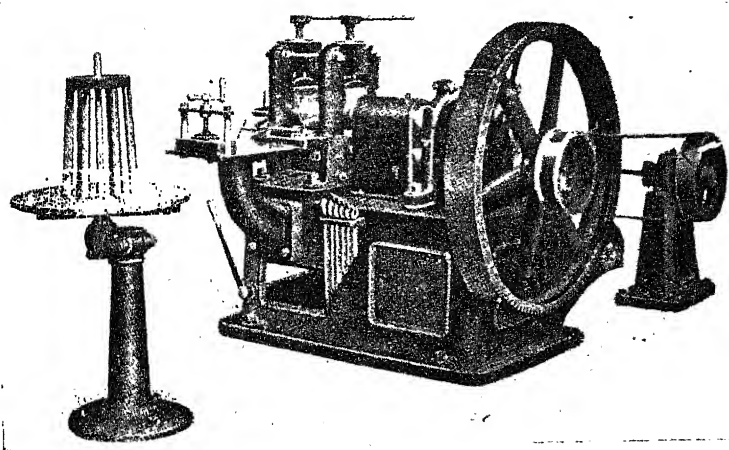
Laminoir pour la fabrication du papier d'aluminium.
